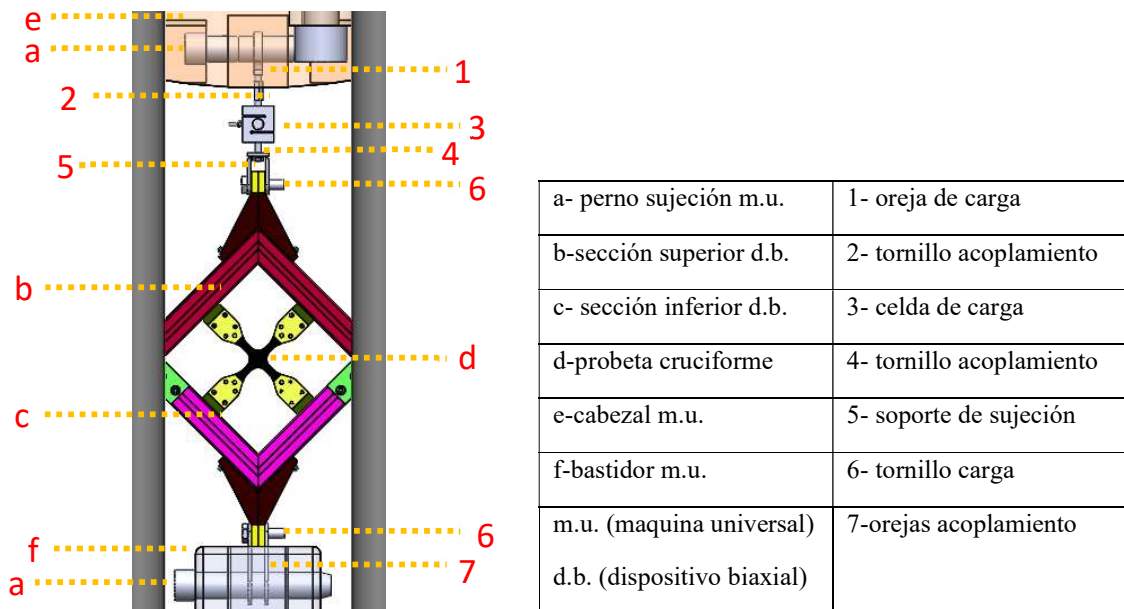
Esquema del dispositivo biaxial acoplado a la maquina universal.
